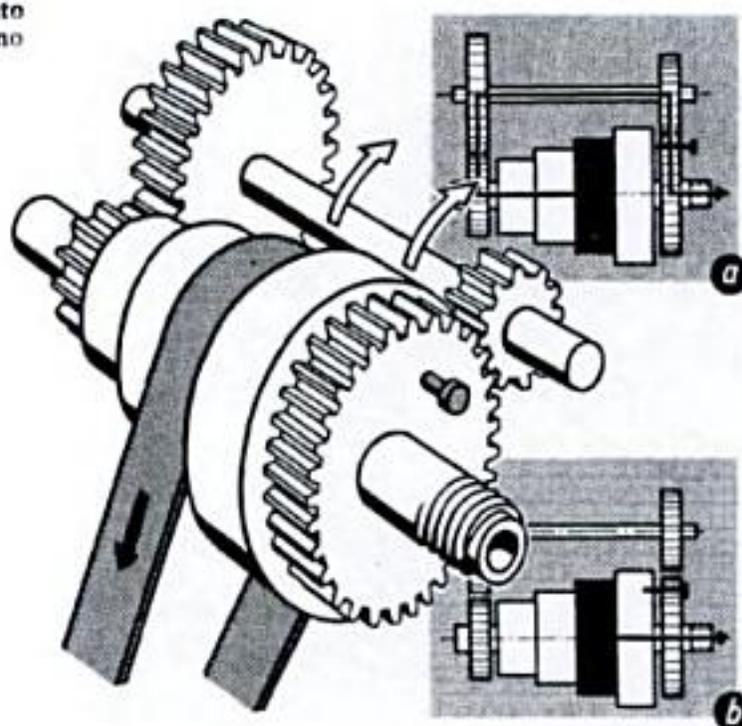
,2 Accionamiento escalonado de cono de poleas con juego de engranajes sencillo
